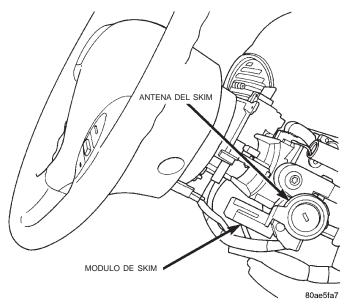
Desmontaje e instalación del Módulo de inmovilizador con llave centinela
